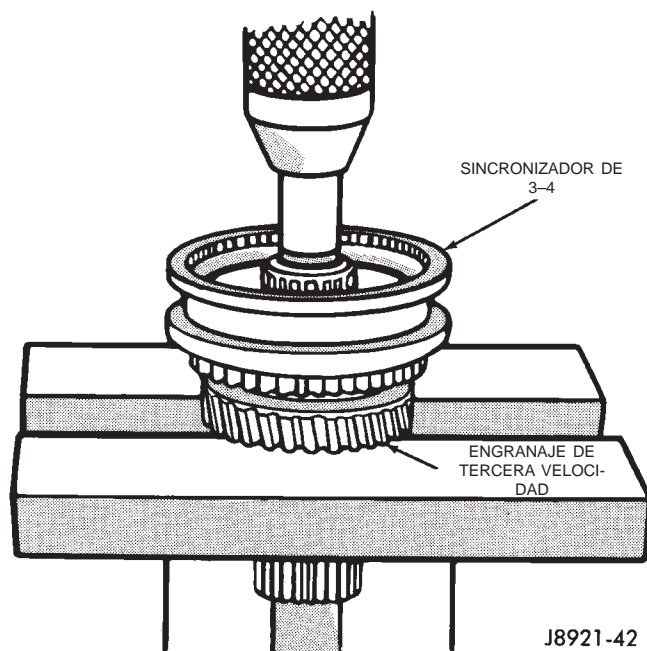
Desmontaje del sincronizador 3-4 y el engranaje de tercera velocidad
